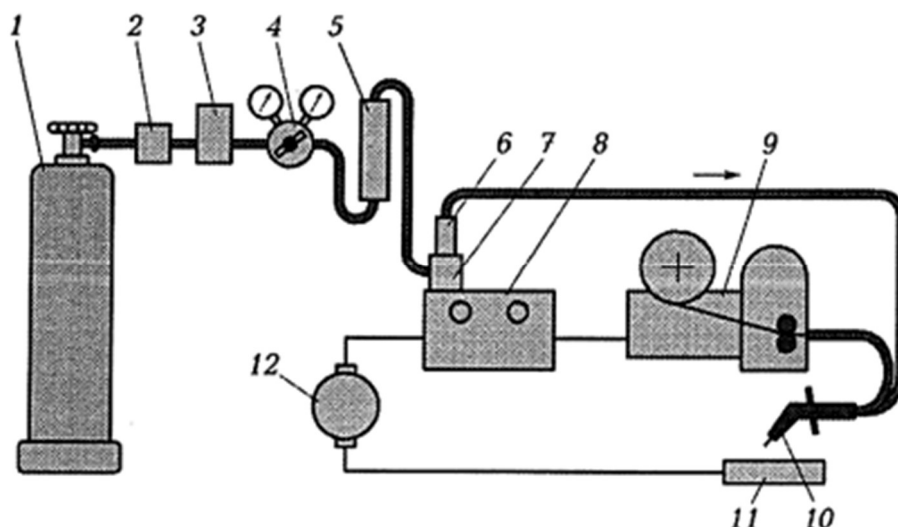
Схема установки для полуавтоматической сварки и наплавки в среде углекислого газа (диоксида углерода):
